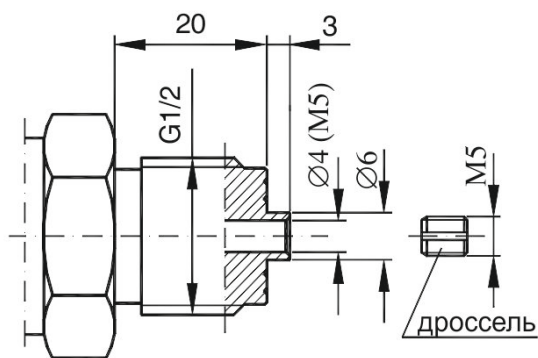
а. Присоединение типа G1/2 с резьбой G1/2"
